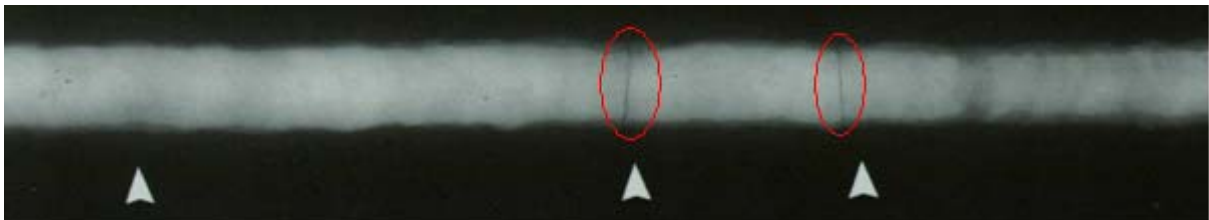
illustration d'un défaut de fissure transversal dans un cordon de soudure.
